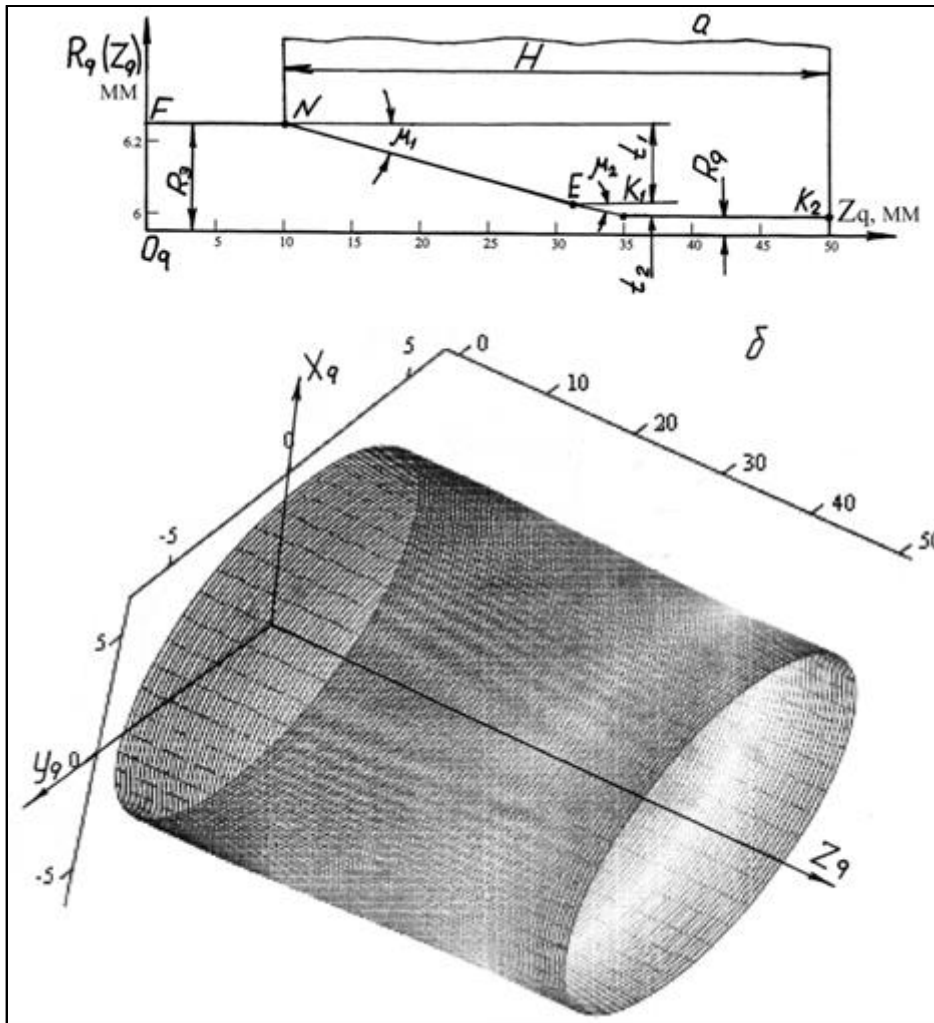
Комбінована поверхня обертання, яка охоплює параметри заготовок і деталей
